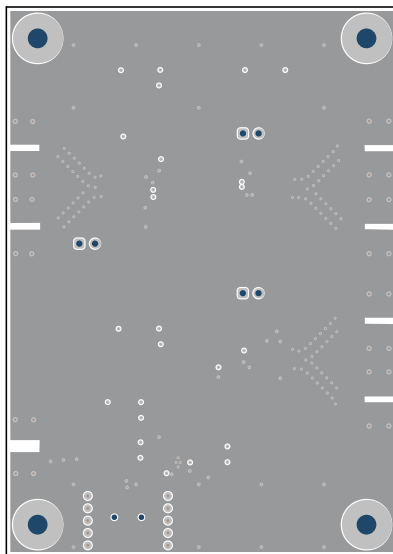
LMK6BEVM の PCB レイアウト例 - グランド層
